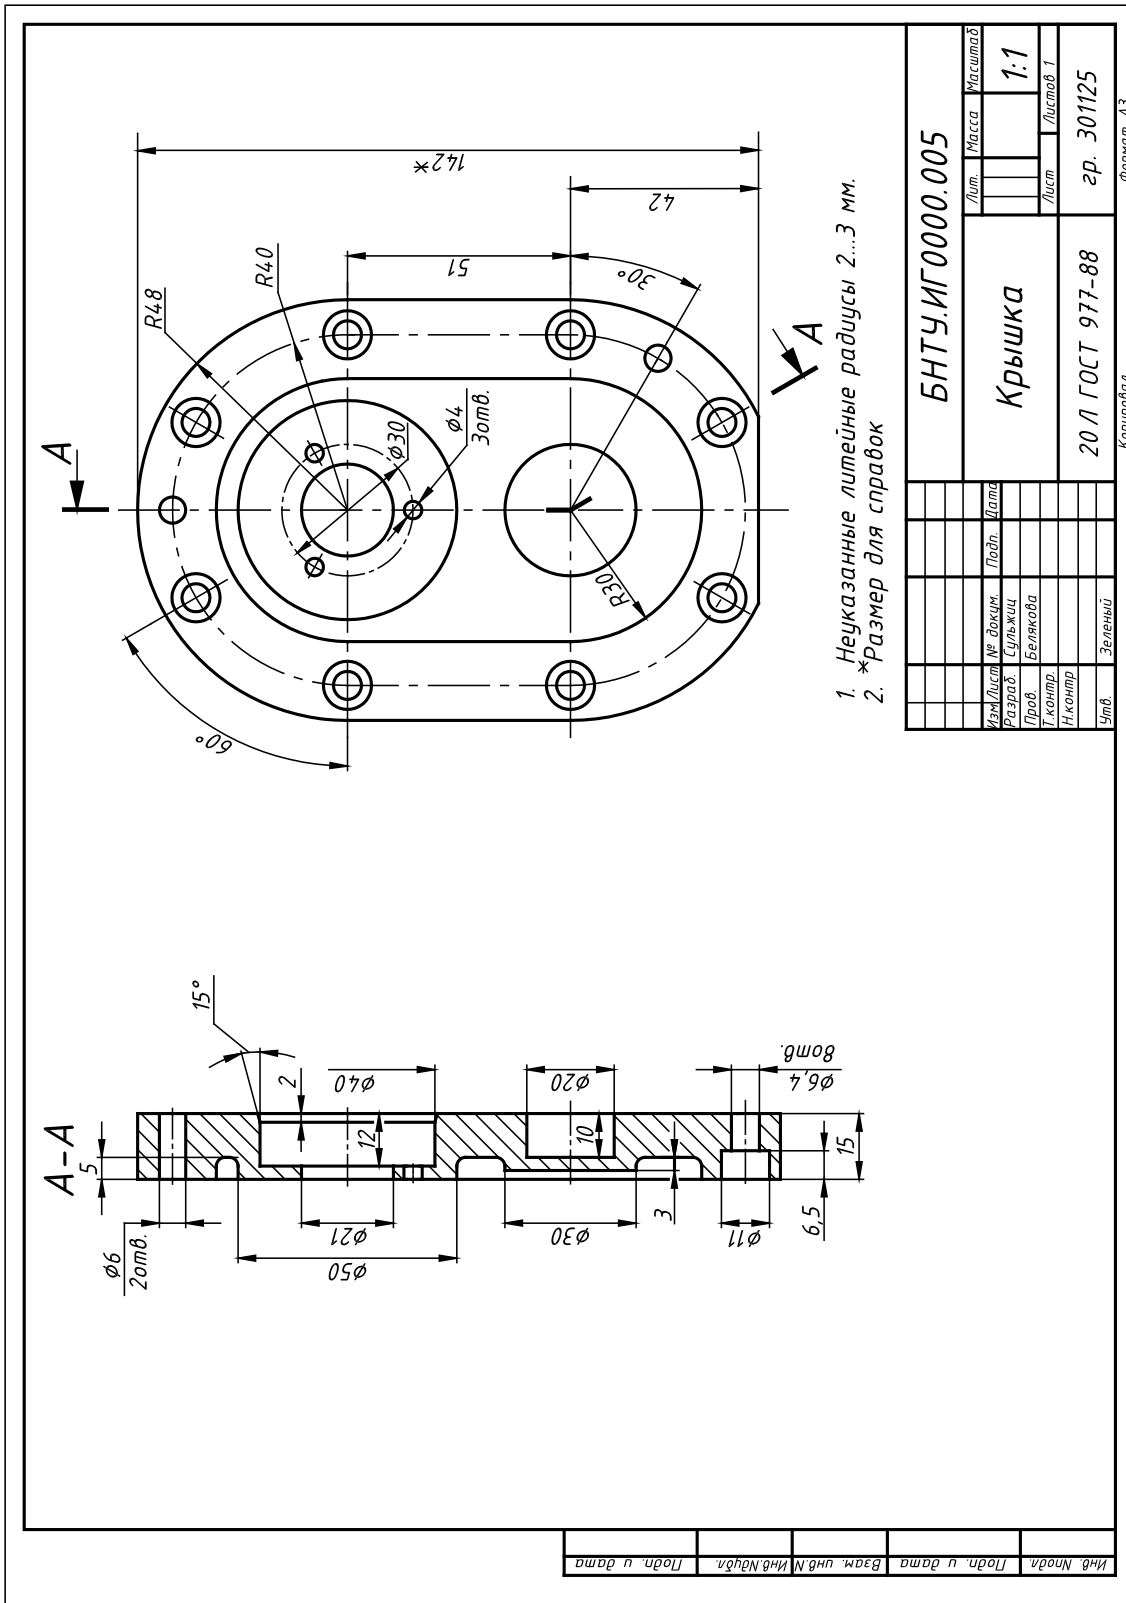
Чертеж крышки (выполнение ломаного разреза)
